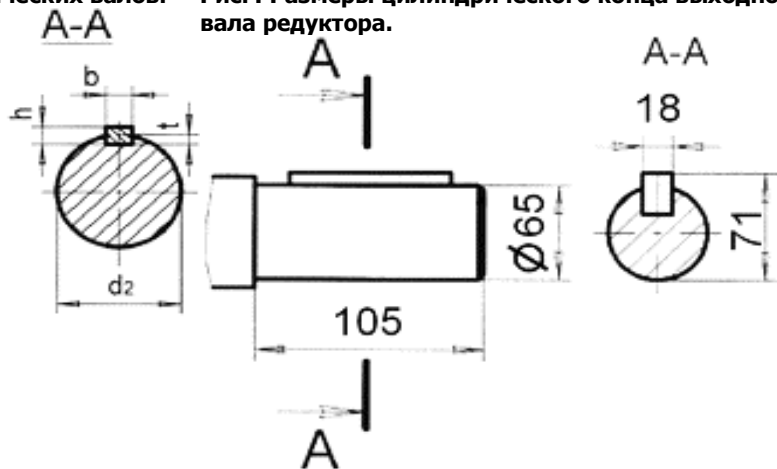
Размеры цилиндрического конца выходного вала редуктора.
